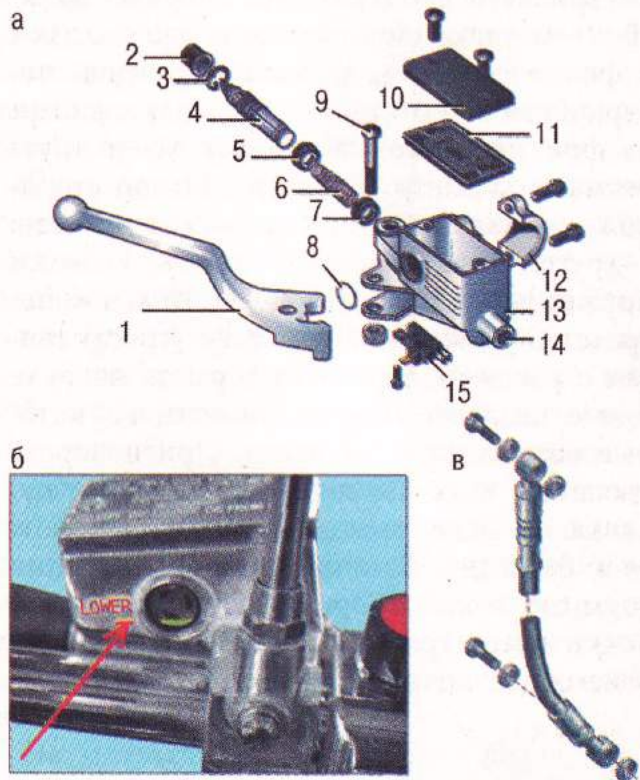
Главный тормозной цилиндр гидравлического дискового тормоза переднего колеса: а – схема; б – глазок (стрелкой указана черта минимального уровня тормозной жидкости); в – тормозной шланг со штуцерами; 1 – рычаг тормоза; 2 – резиновый колпачок; 3 – стопорное кольцо; 4 – поршень; 5 – уплотнительное кольцо; 6 – возвратная пружина; 7 – главное уплотнительное кольцо; 8 – глазок; 9 – ось рычага; 10 – крышка; 11 – диафрагма; 12 – кронштейн крепления к рулю; 13 – бачок главного тормозного цилиндра; 14 – выходное отверстие с резьбой; 15 – концевой выключатель цепи стоп-сигнала
